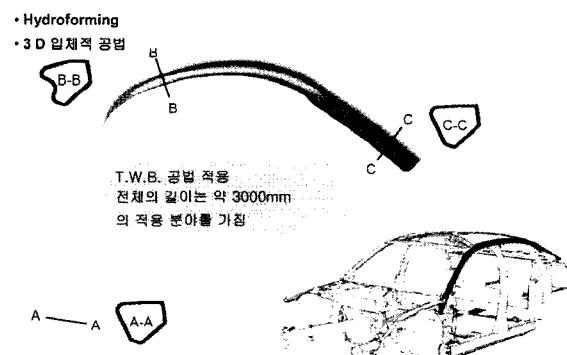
3차원 하이드로포밍에 의한 reinforcement front pillar & roof rail outer
